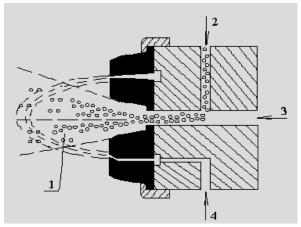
Схема процесса газопламенного нанесения покрытий из порошковых материалов: 1 — газовое пламя; 2 — подача порошка; 3 — подача сжатого воздуха; 4 — подвод горючей смеси газов
